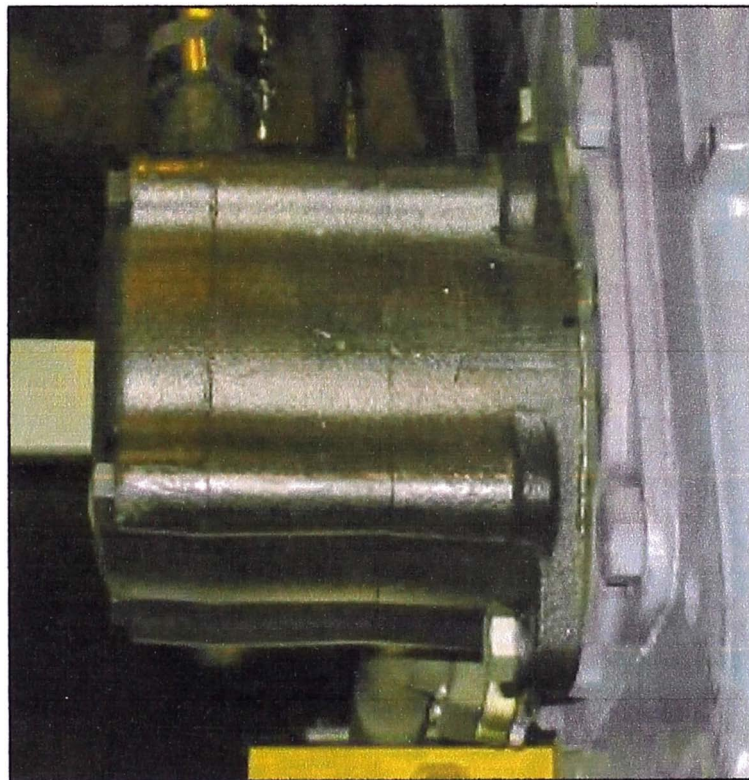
Bomba del Motor del Ventilador del Radiador del Motor
